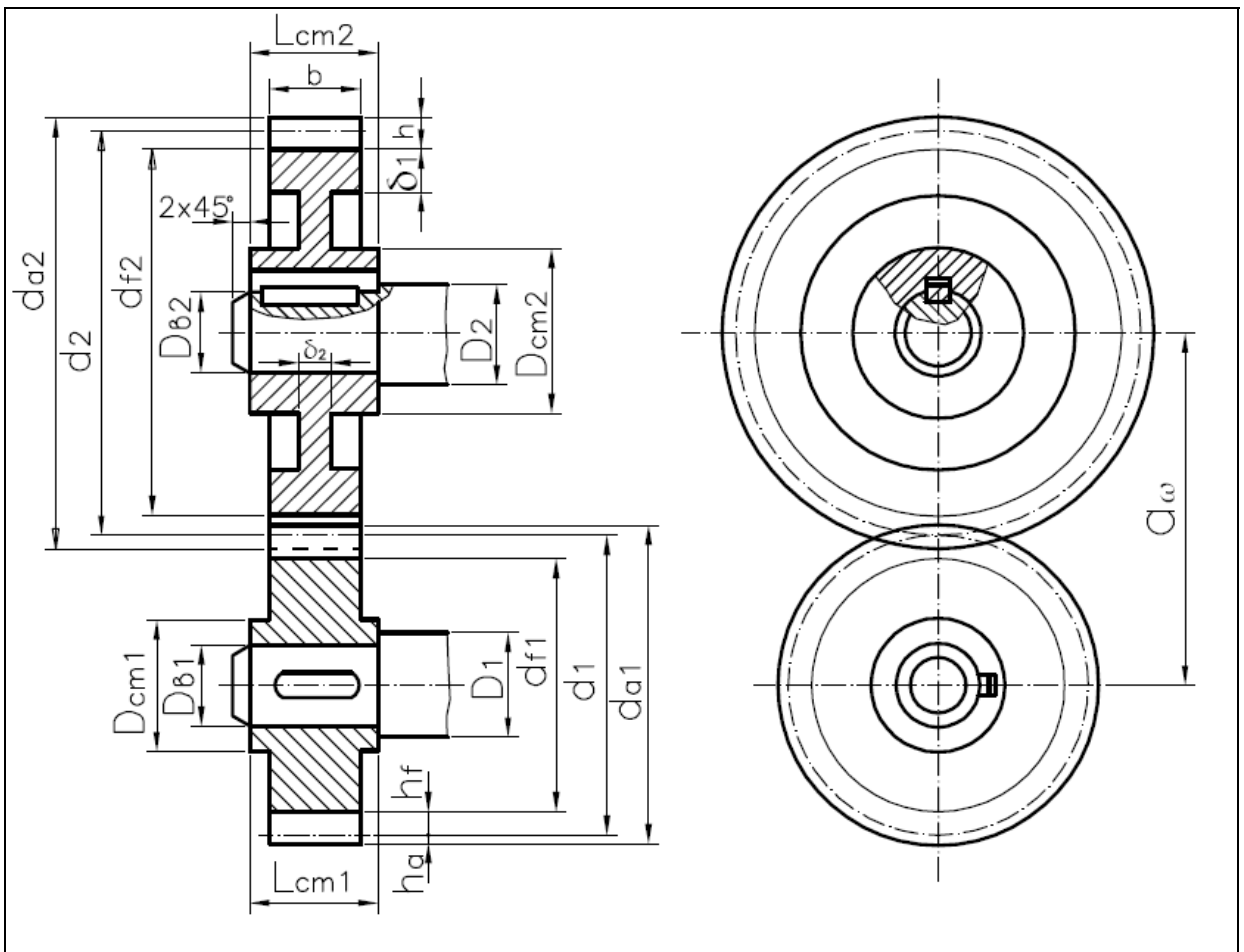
Геометрические параметры цилиндрической зубчатой передачи.
